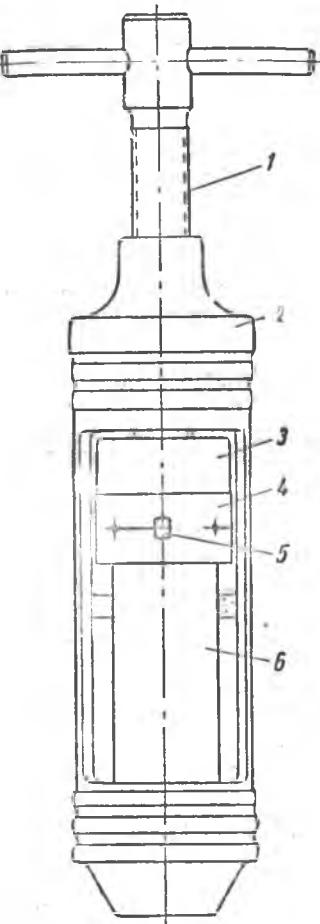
Общий вид закрутки: 1 — винт; 2 — корпус закрутки; 3 — матрица; 4 — насадка «звездочка»; 5 — шарик гитарной струны; 6 — патрон.
